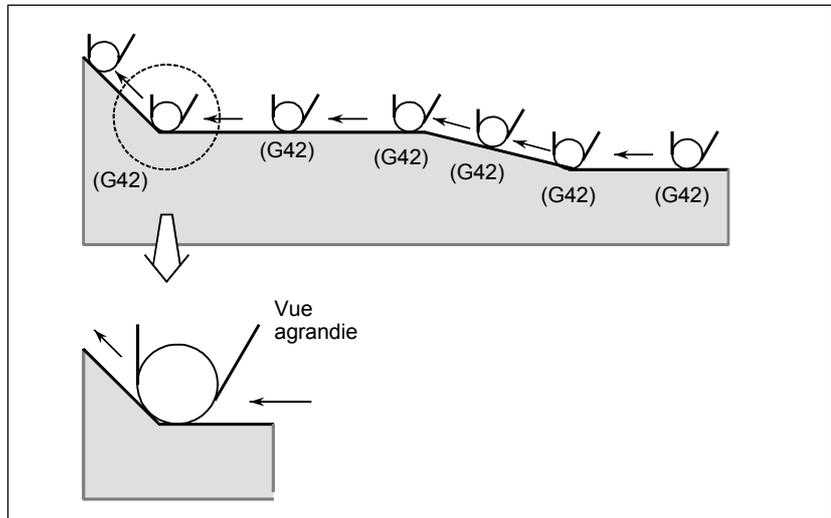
(c) Déplacement de l'outil lorsque la position de la pièce ne change pas
